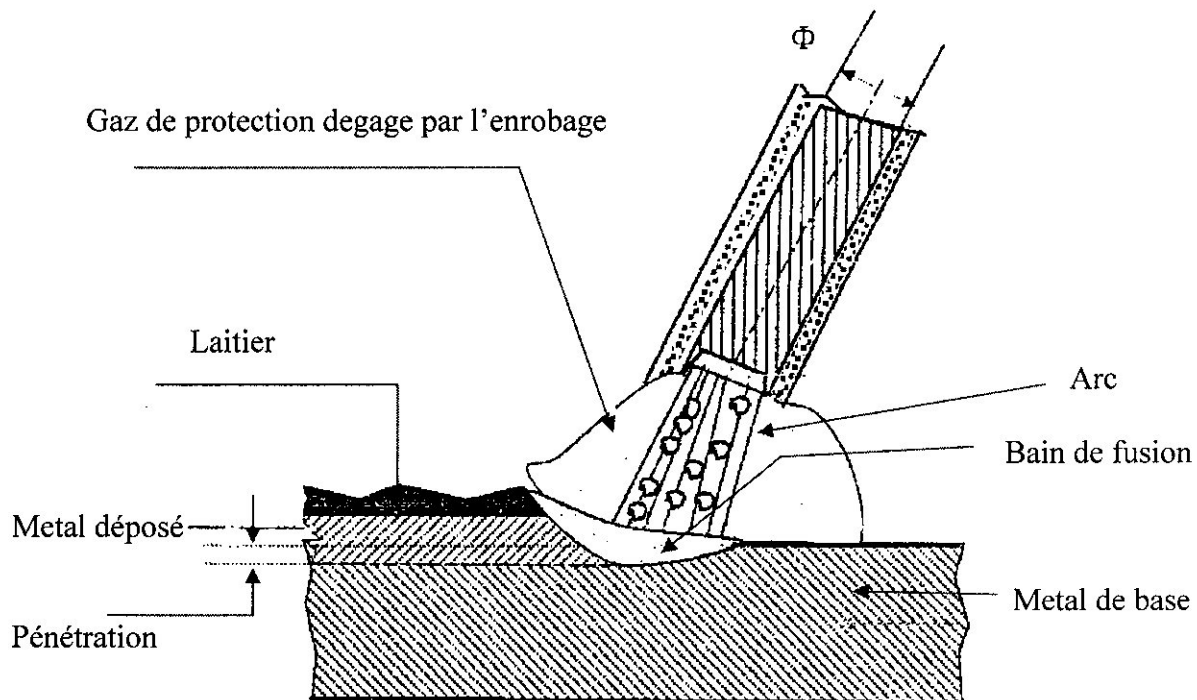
soudage à l'arc avec électrode enrobée
